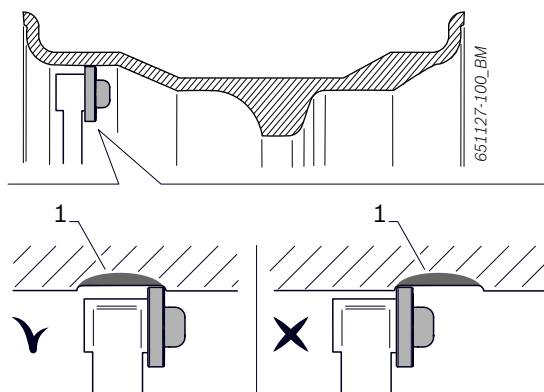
Posizione tastatore rispetto all'area di fissaggio del peso adesivo
